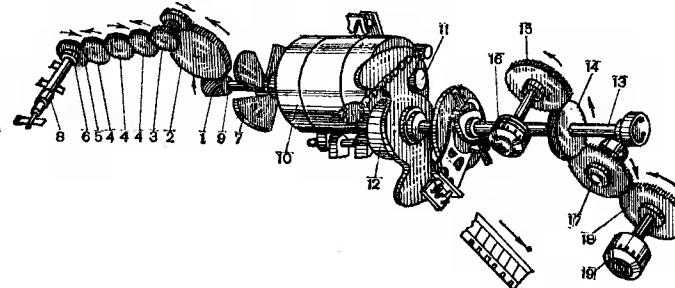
Кинематическая схема кинопроектора П16П1: 1 — червяк; 2 — промежуточная шестерня; 3 — двойная шестерня; 4 — промежуточные шестерни; 5 — шестерня фрикционная; 6 — фрикцион наматывателя; 7 — вентилятор; 8 — вал наматывателя; 9 — вал электродвигателя; 10 — электродвигатель; 11 — шкив электродвигателя; 12 — шкив обтюратора; 13 — ведущий вал; 14 — червячная шестерня; 15 — шестерня вала тянутого барабана; 16 — тянутый барабан; 17 — промежуточная шестерня; 18 — шестерня вала задерживающего барабана; 19 — задерживающий барабан
